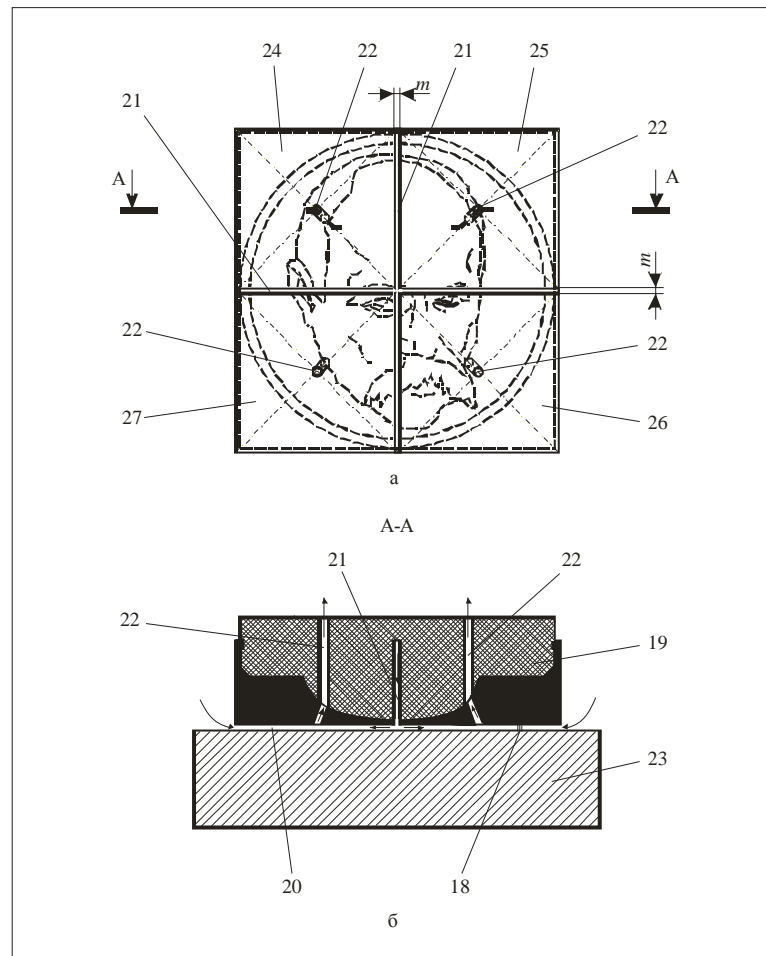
Розмірна обробка дугою великогабаритної торцевої поверхні складного рельєфу (прес-форми) з використанням багатоканального двошарового електрода-інструмента: а - вид на двошаровий електрод-інструмент знизу; б - початкова фаза обробки
